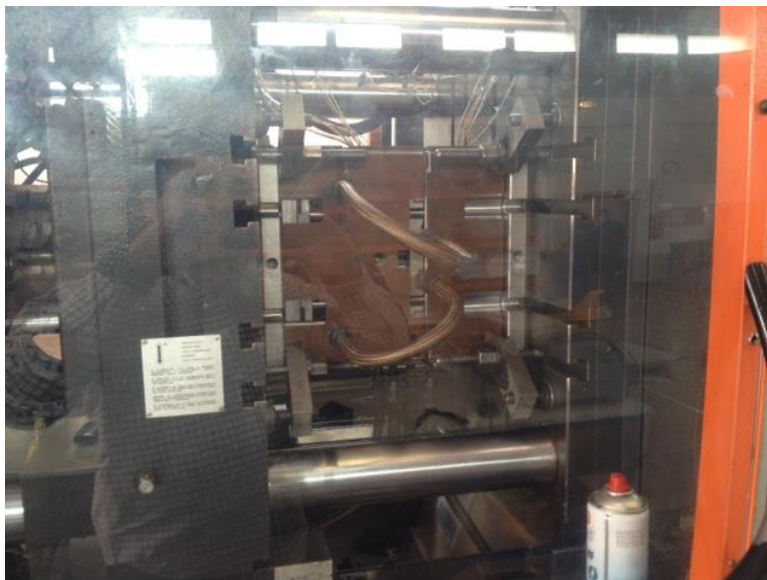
Molde M1724 na máquina de injeção, a aquecer para se iniciar o 1º teste.
